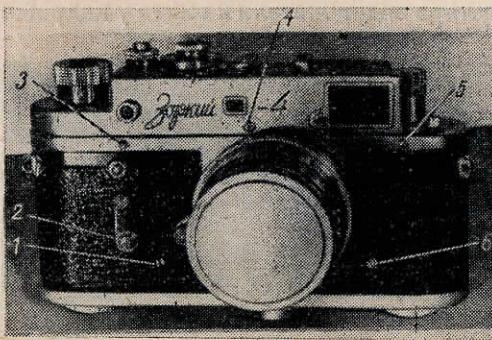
Винты на корпусе фотоаппарата «Зоркий-4»
